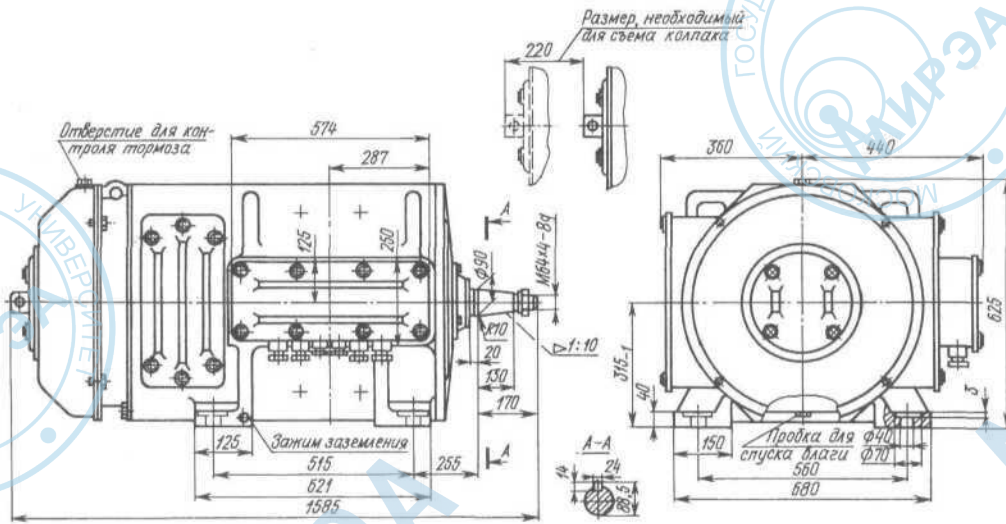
Габаритные, установочные, присоединительные размеры двигателя ДПМ 62 с тормозом
